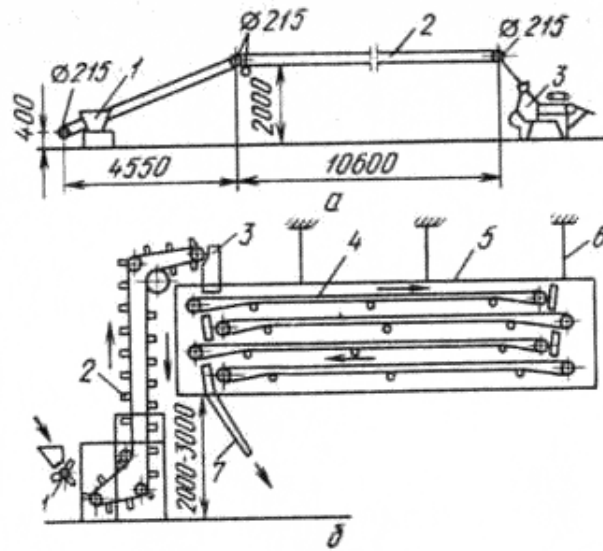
Обладнання для для попереднього вистоювання тістових заготовок: а) відкритий стрічковий транспортер; б) шафа з стрічковими транспортерами
